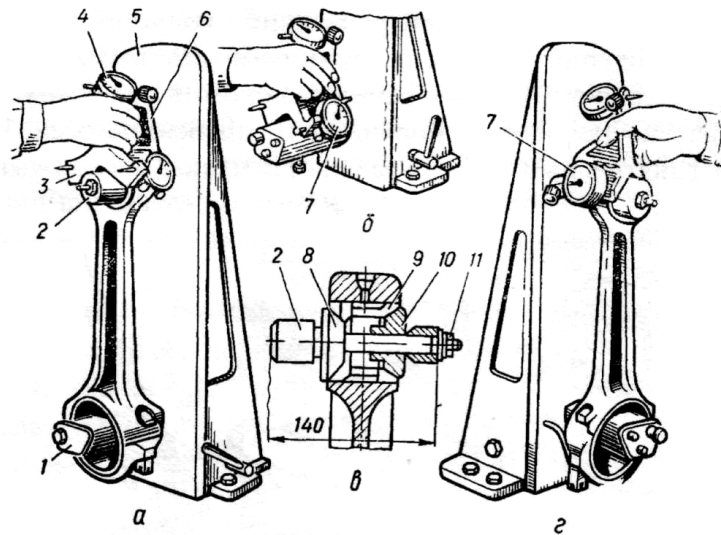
Будова пристрою КИ-724 для перевірки шатуна на згин і скрученість: а – перевірка шатуна на згин; б – встановлення індикаторів; в – встановлення розтискної оправки; г – перевірка шатуна на скрученість; 1 – оправка.; 2 – розтискна оправка; 3 – призма; 4, 7 – індикатори; 5 – плита; 6 – упор; 8, 10 – конуси; 9 – розтискна втулка оправки; 11 – гайка
